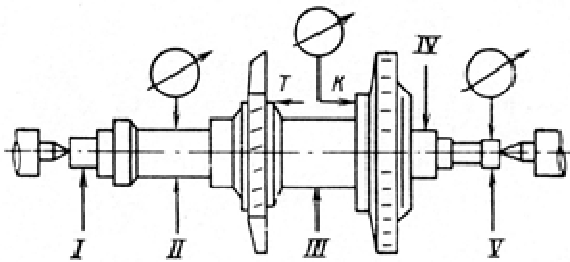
Схема контролю ротора турбокомпресора: 1 – вал ротора; 2 – вимірювальний індикатор часового типу; 3 – колесо турбіни; 4 – колесо компресора; 5 – центри токарного верстата; I-V – місця замірів биття вала; Т,К – місця заміру торцевого биття відповідно колеса турбіни і колеса компресора
